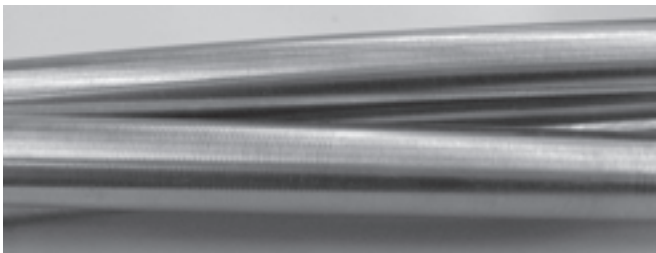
Aspecto visual da superfície do provete após maquinagem com a ferramenta comercial.
